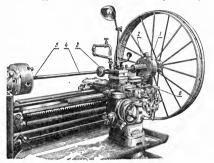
Приспособление для расточки ступиц колес; 1 — кулачковый патрон; 2 — корпус; 3 — поводок; 4 — борштанга; 5 — вгулка; 6 — болт.
